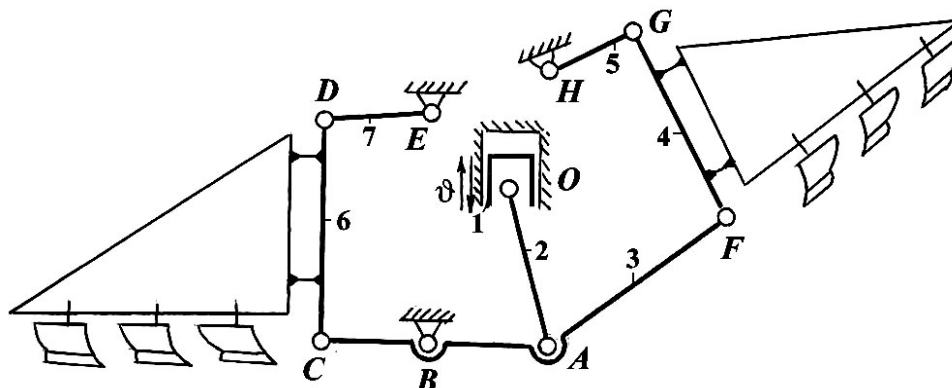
Механизм навески плугов для гладкой пахоты (челночный плуг)
